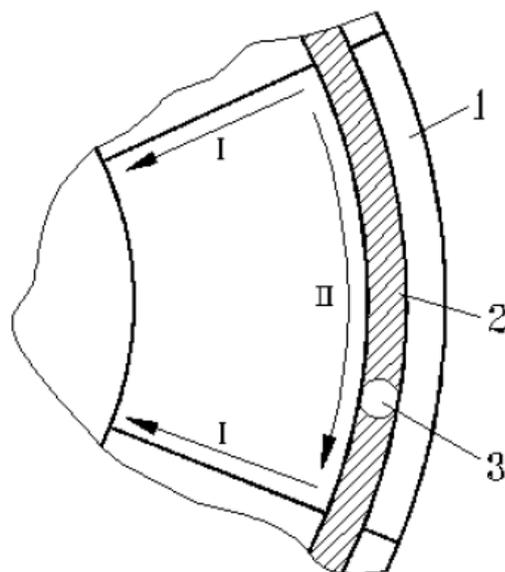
Последовательность и направление сварки швов
